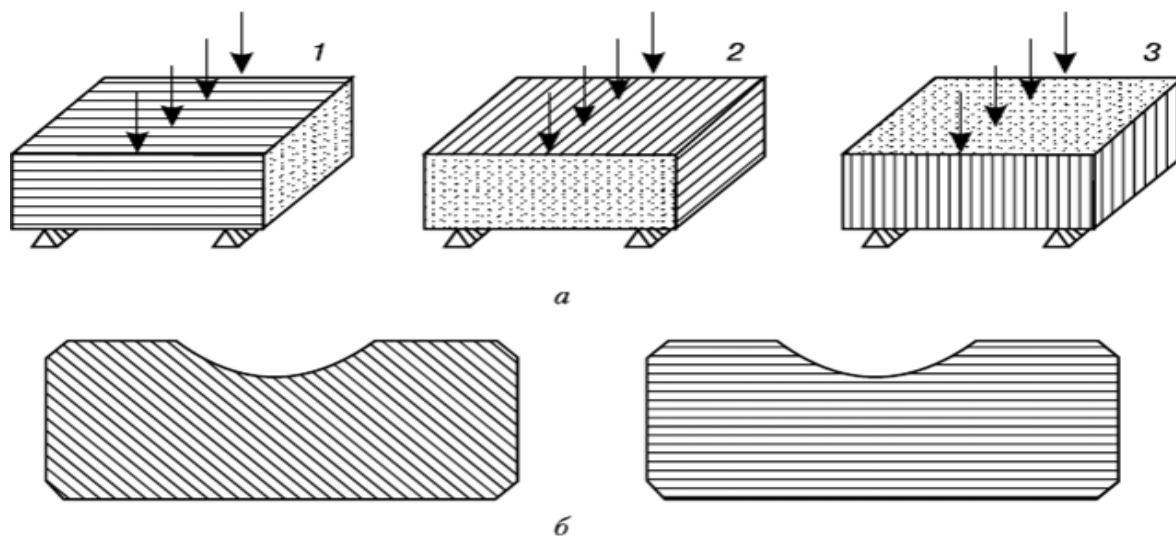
Ориентировка волокон в образцах (*a*) и кольцах подшипника (*б*)
